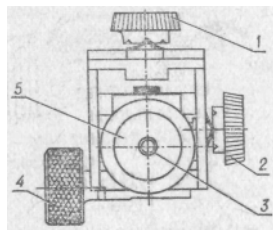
Крепление и регулировка прицела пневматических винтовок «311» и «312» (ГДР)
